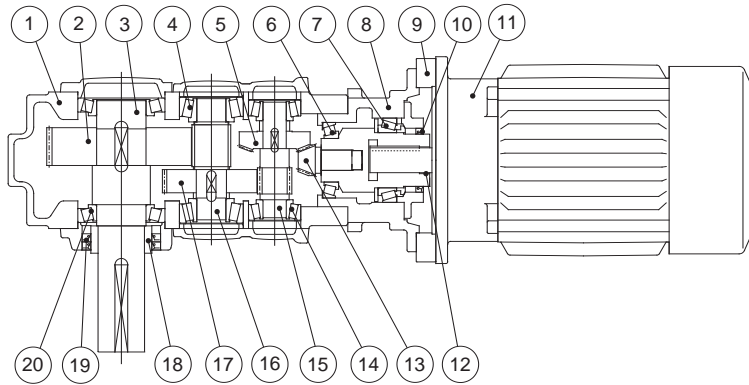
Getriebemotor mit rechtwinkliger Wellenanordnung
